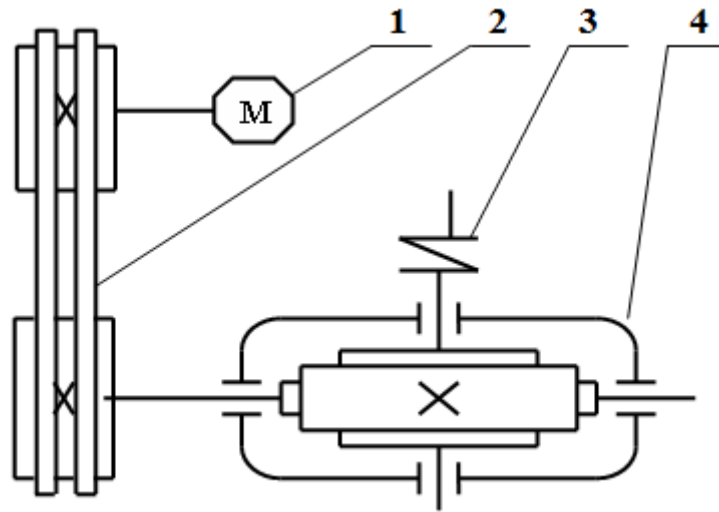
Привод гвинтового конвеєра: 1 – електричний двигун, 2 – пасова передача, 3 – муфта типу МПВП, 4 – одноступінчатий черв'ячний редуктор з верхнім розташуванням черв'яка.
